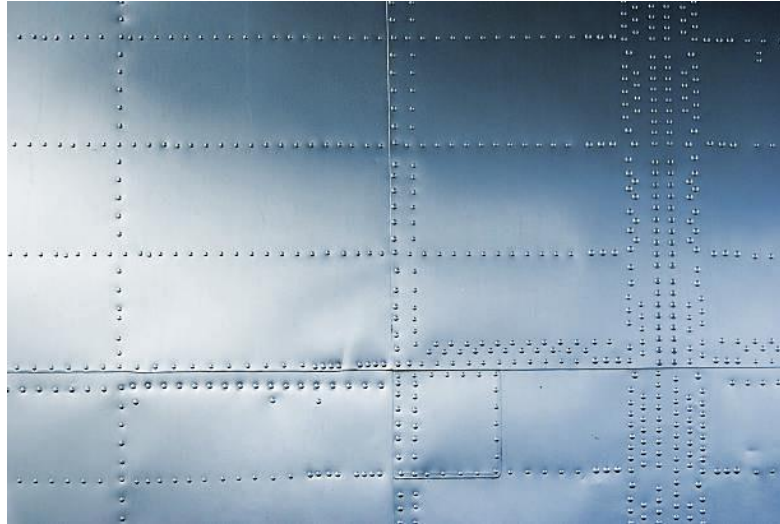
Конструкция цилиндрической оболочки с локальными опорами
